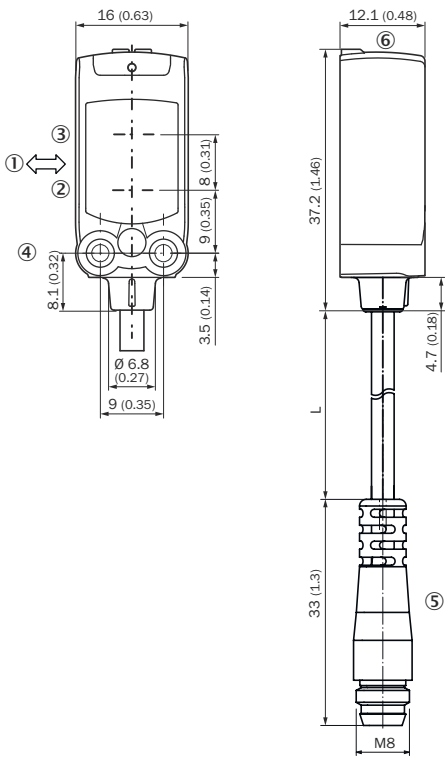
Disegno dimensionale 1, cavo con connettore maschio M8
